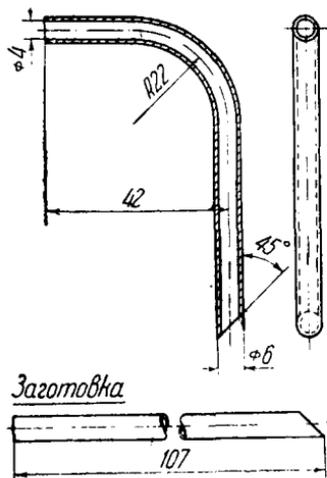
Дет. № 16-14. Трубка воздушная крышки поплавковой камеры
